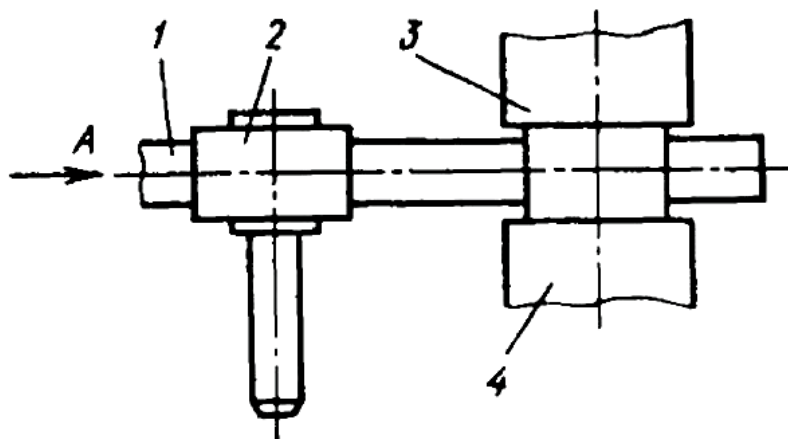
Схеми згинання: 1 – упор; 2 – заготовка; 3, 4 – верхній і нижній бойки
